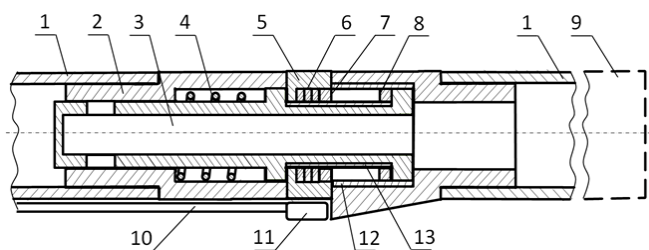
Обратный клапан электроцентробежной установки с электромагнитом: 1 – насосно-компрессорная труба; 2 – корпус клапана; 3 – золотник; 4 – возвратная пружина; 5 – корпус электромагнита; 6 – катушка электромагнита; 7 – полюс электромагнита; 8 – ответное ферромагнитное кольцо; 9 – фильтр; 10 – кабель; 11 – коробка контактных зажимов; 12, 13 – внутренняя и внешняя диэлектрические трубки
